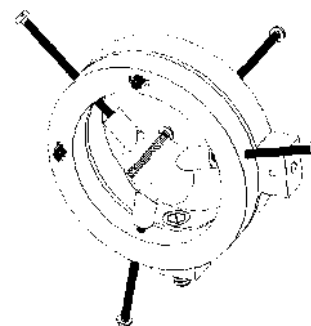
модель крепежа лазера в цилиндрическом корпусе
